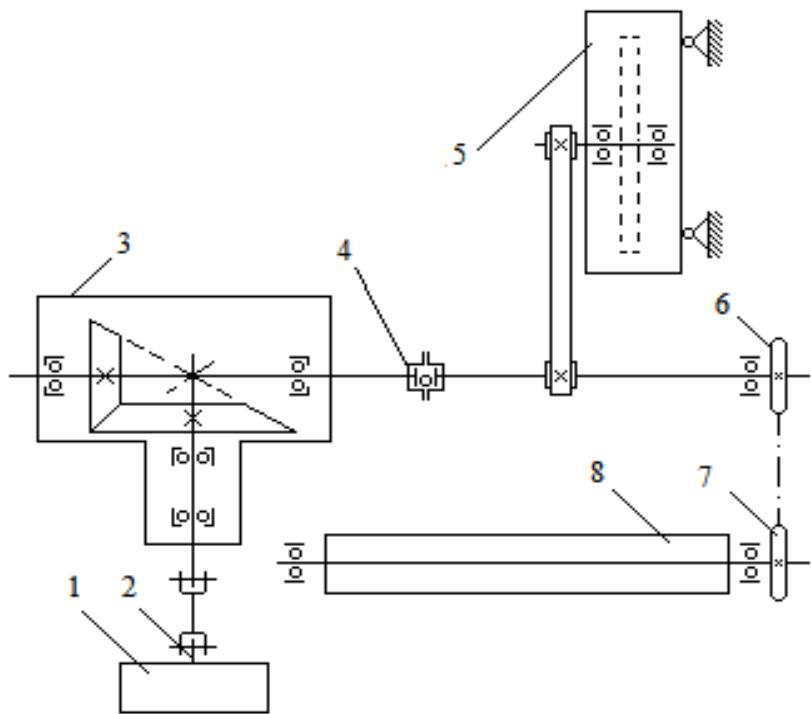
Кинематическая схема передачи движения основным узлам сеялки для посева бахчевых культур: 1-трактор; 2-вал отбора мощности (ВОМ) трактора; 3-конический редуктор; 4-обгонная муфта; 5-вакуум-насос; 6-ведущая звездочка; 7-ведомая звездочка; 8-фреза.
